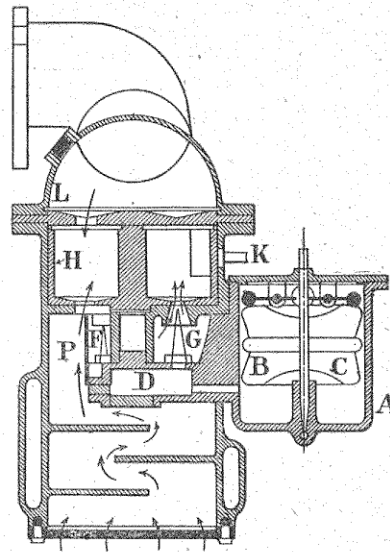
Coupe de carburateur Daimler à trois gicleurs.
